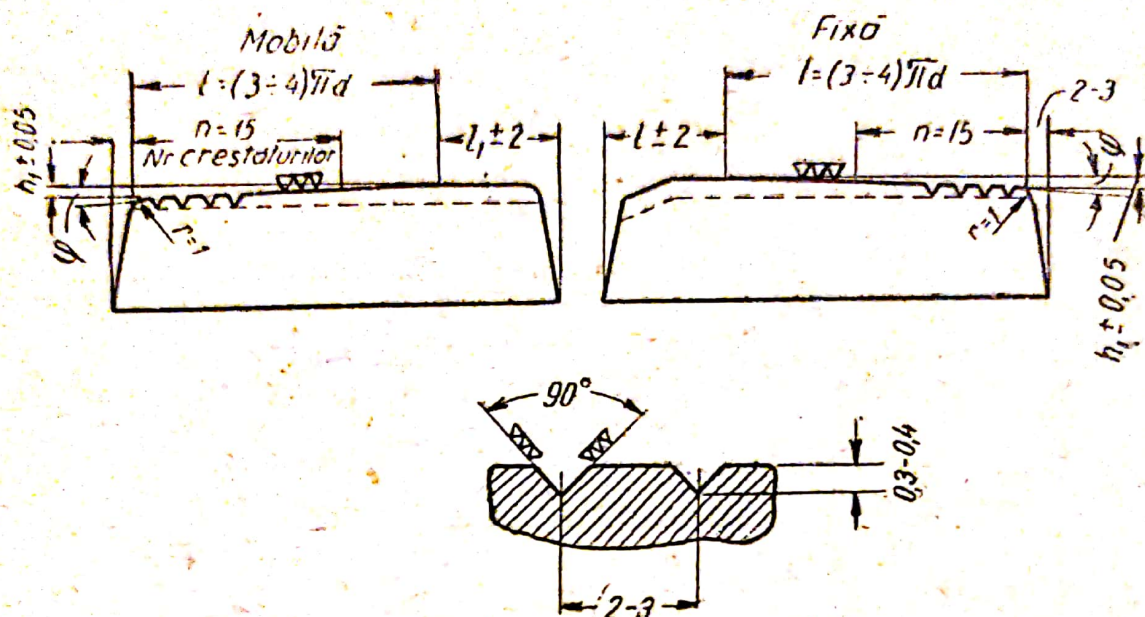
Placă cu o porțiune lungă de profilare cu o înclinație pe înălțimea profilului filetului
